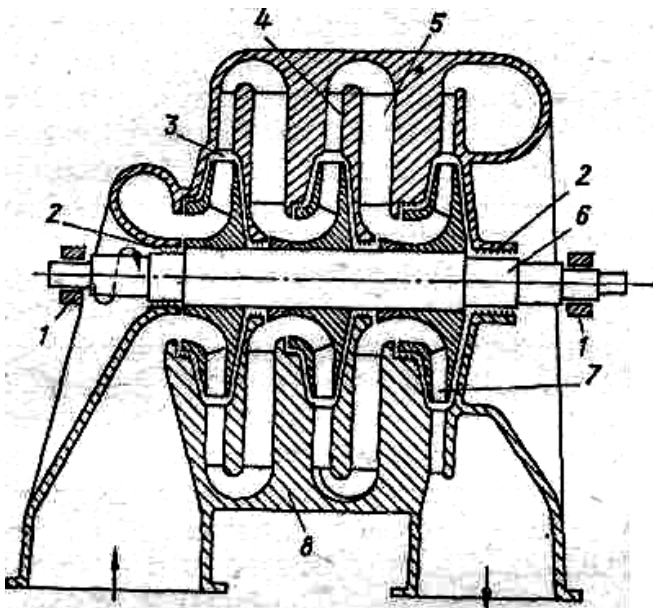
Схема відцентрового компресора: 1–підшипник, 2–ущільнення, 3–безлопатковий дифузор, 4–лопатковий дифузор, 5–зворотній направляючий апарат, 6–ротор, 7–робоче колесо, 8–корпус
